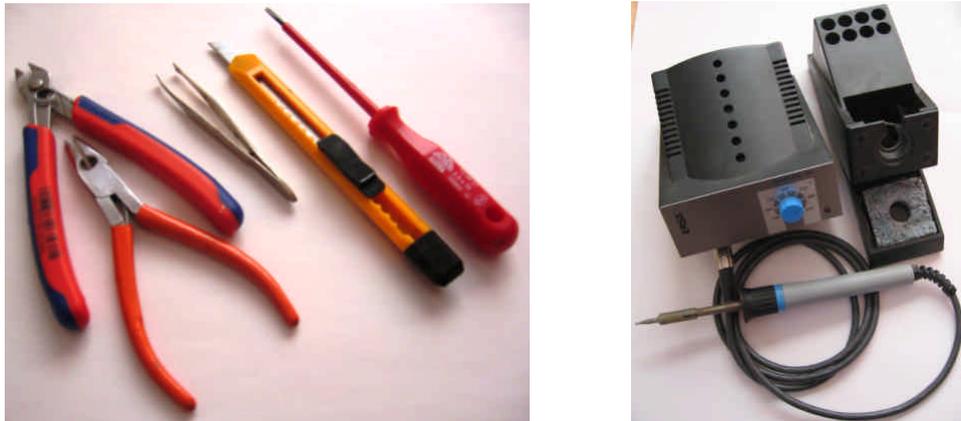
Notwendige Werkzeuge zum Aufbau des AKKON USB Controller Board
